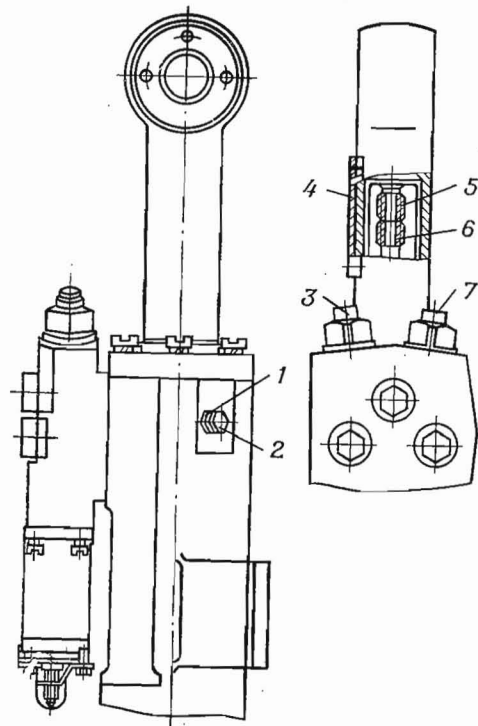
Выпуск воздуха из исполнительного цилиндра:
